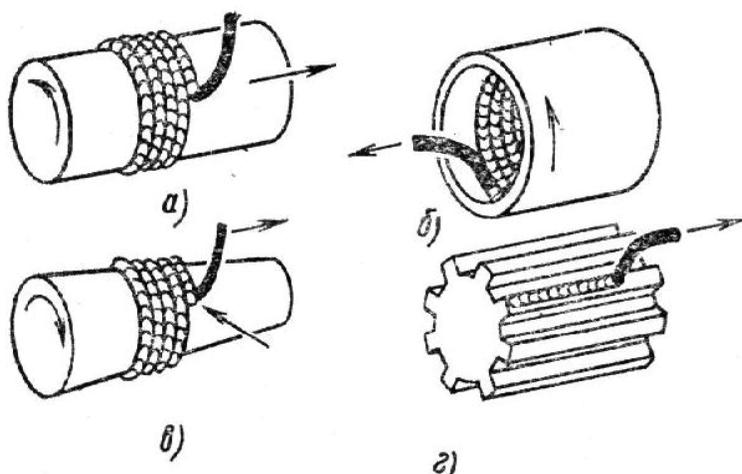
Схемы вибродуговой наплавки изделий различной формы:
